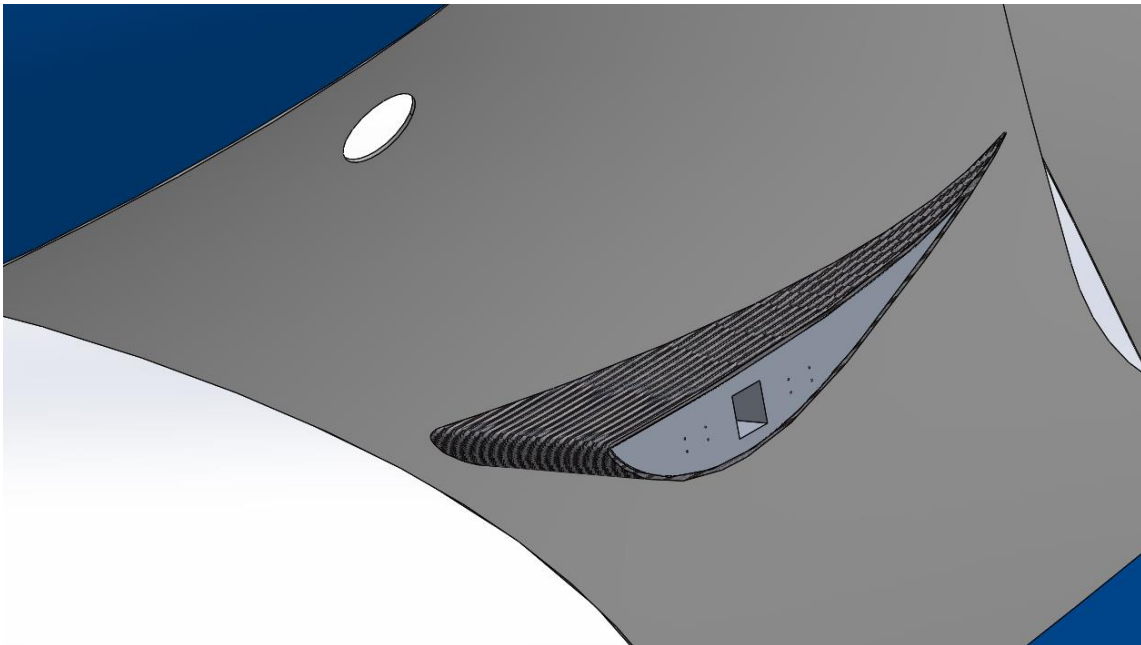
Conjunto tapa-alerón del mecanismo de engranajes
